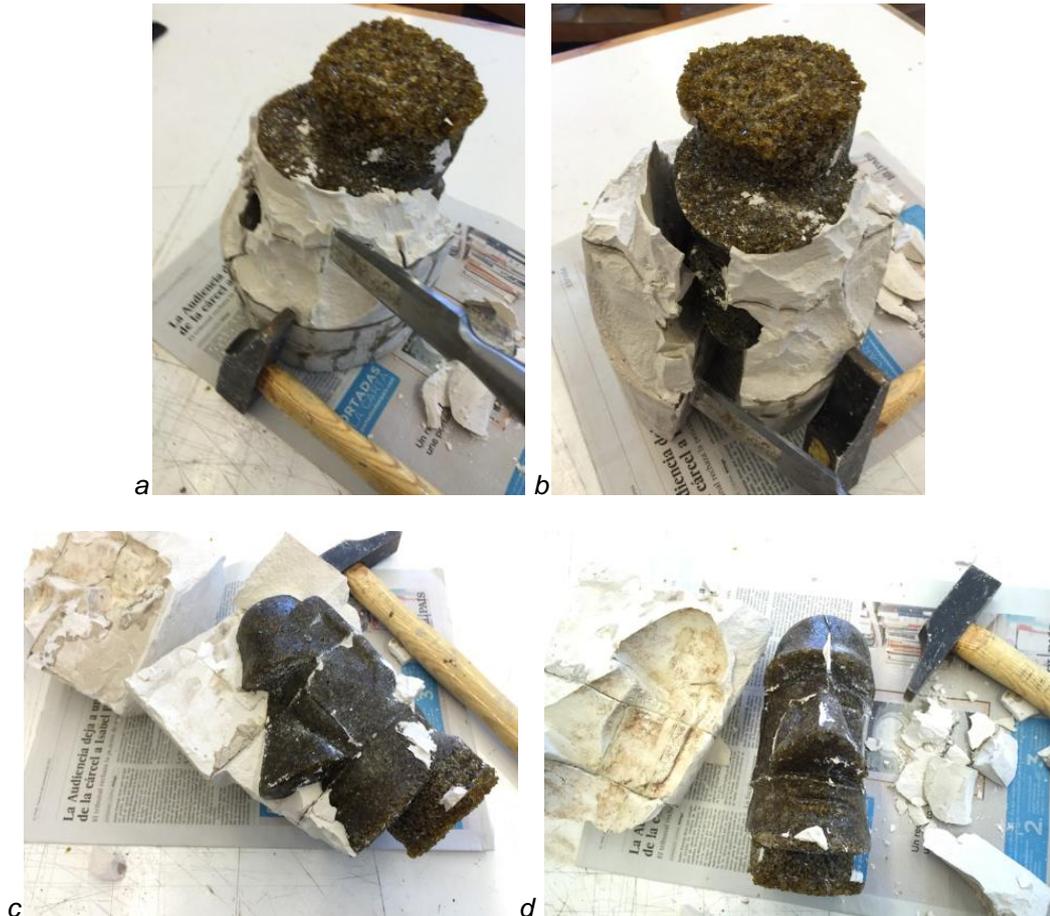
Desmoldado de la figura Pascua. a) y b) Fractura de la base del molde. c) y d) Fractura del resto del molde.
